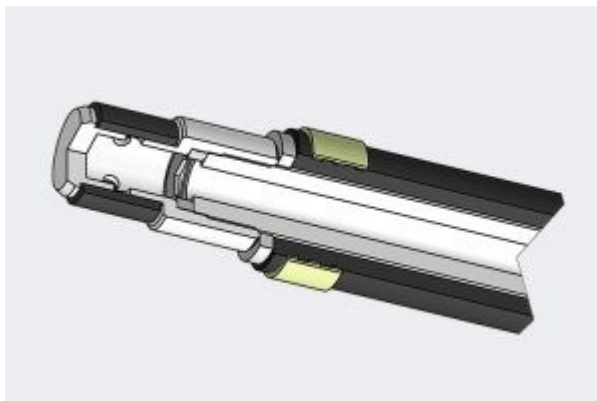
Основной корпус прибора содержит и узел пакеровки
